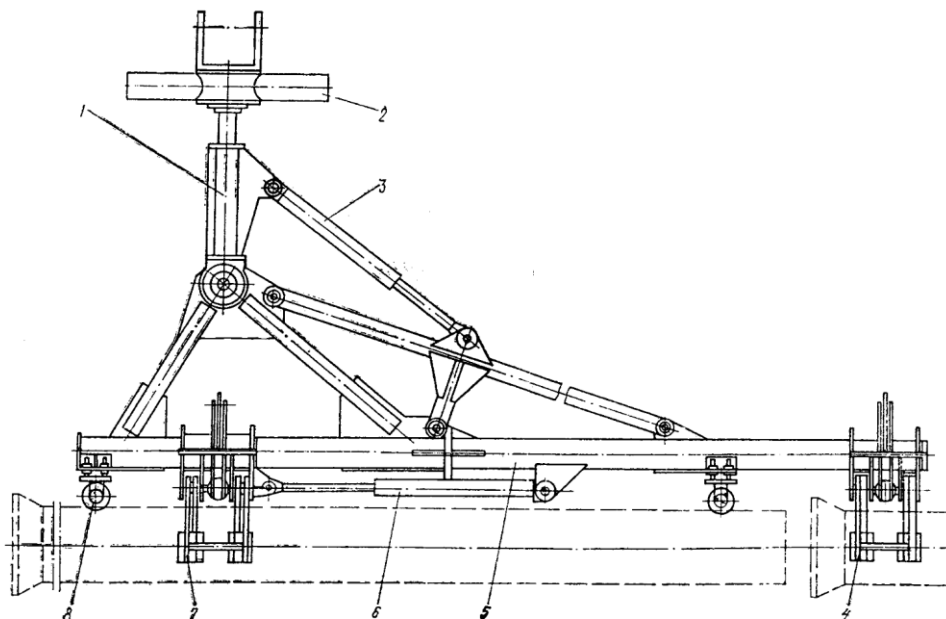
Навесное оборудование для подачи, укладки и стыковки труб: 1 – амортизатор; 2 – поворотная головка; 3 – гидроцилиндр перекоса траверсы; 4 – неподвижный захват; 5 – траверса; 6 – гидроцилиндр механизма стыковки; 7 – подвижный захват; 8 – ограничивающие ролики
